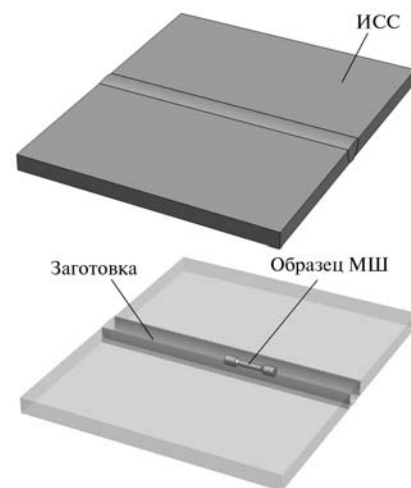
Схема вырезки цилиндрических образцов из сварного шва
